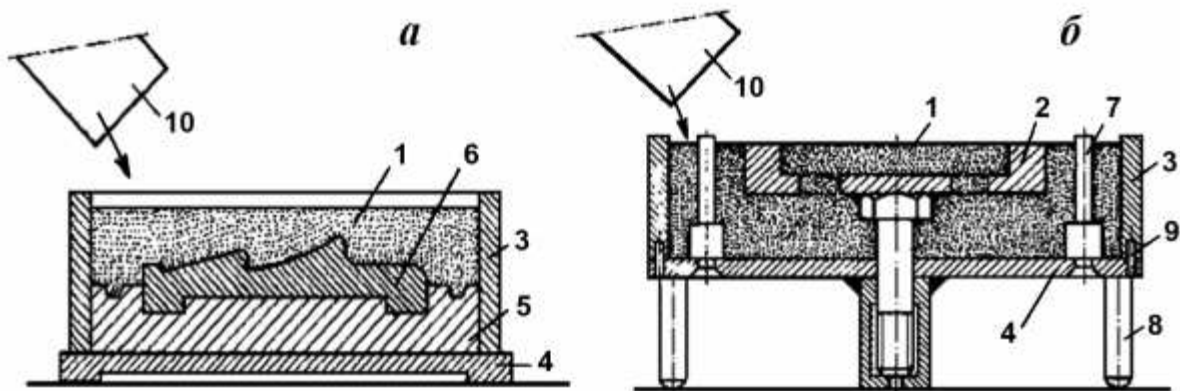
Схема вільного лиття у відкриту форму: а) виріб однорідний; б) виріб з металевою арматурою; 1 – відливка; 2 – елемент який заливається; 3 – корпус форми; 4 – підкладка; 5 – матриця; 6 – шаблон; 7 – арматура; 8 – ніжки опору; 9 – центральні штифти; 10 – ємність з заливною композицією [13].
